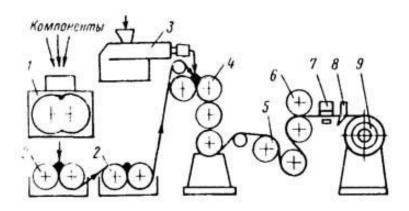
Технологическая схема изготовления полосовой заготовки полимерного материала каландрованием:
